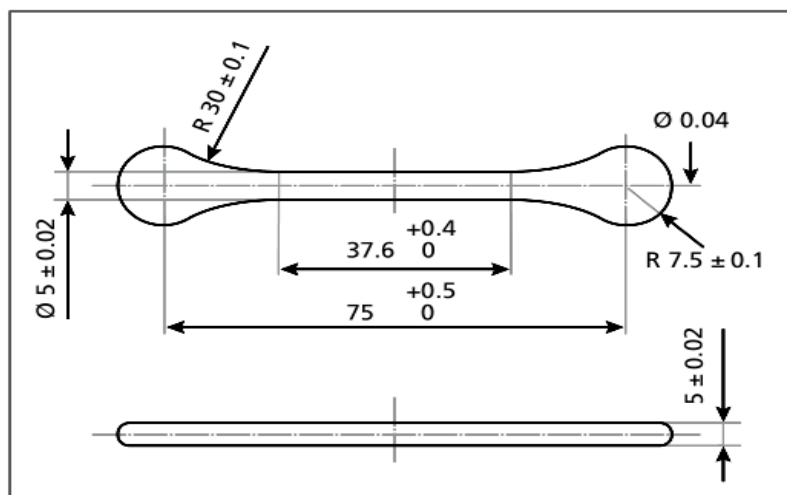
Образец, полученный литьём под давлением металла, для испытаний на растяжение согласно ISO 2740
